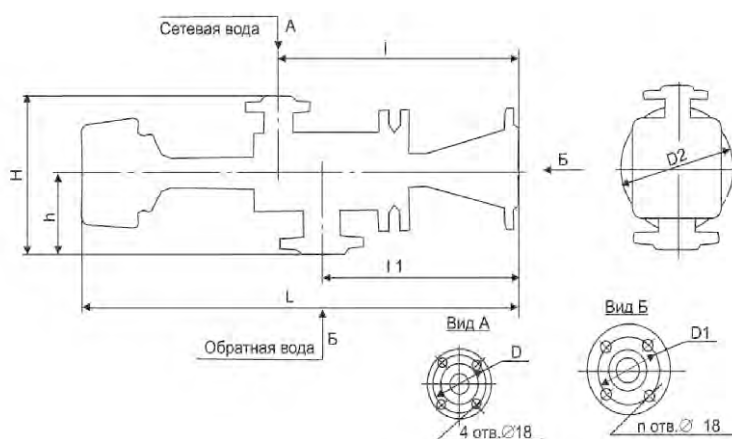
Габаритные и присоединительные размеры термомайзеров Р-7.Т.
